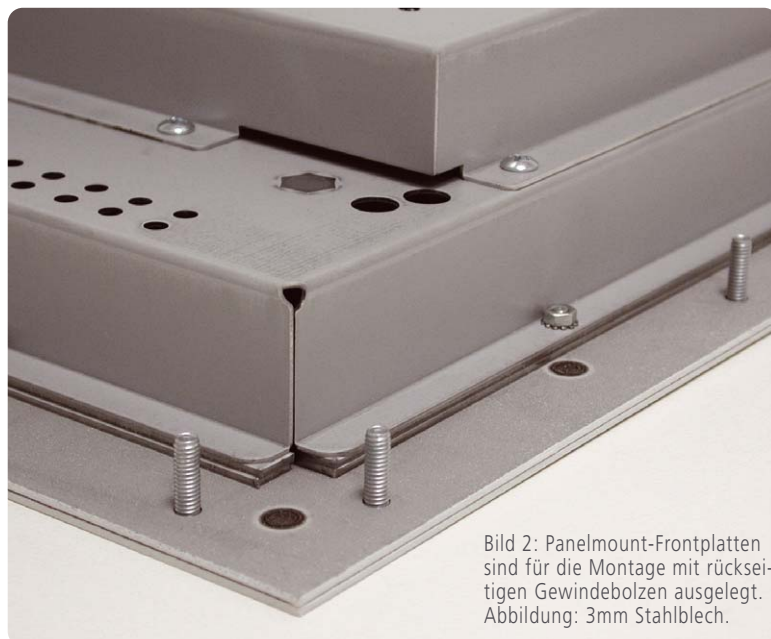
Panelmount-Frontplatten sind für die Montage mit rückseitigen Gewindebolzen ausgelegt. Abbildung: 3mm Stahlblech.
